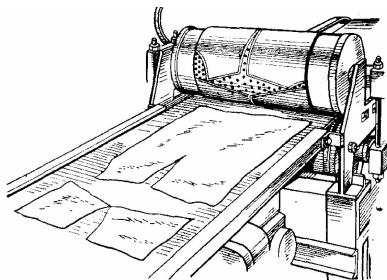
Схема установки для ротаційного способу розкроювання матеріалів
